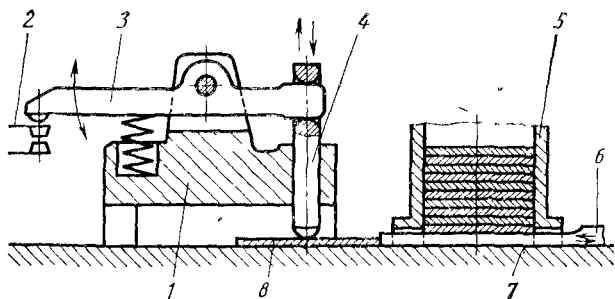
Электромеханический КБУ для контроля толщины заготовки
